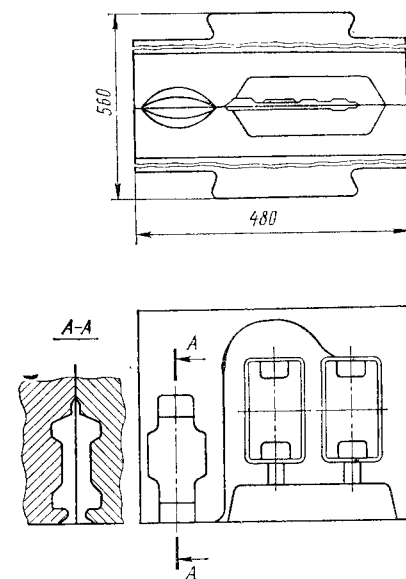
Ковочный штамп для штамповки подушки задней рессоры
